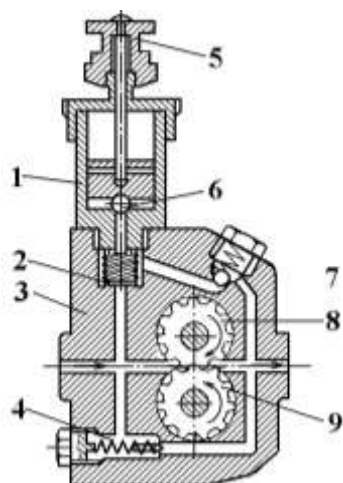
Шестеренчатый ТПН с внешним зацеплением: 1 – ручной прокачивающий насос; 2, 7 – клапаны ручной подкачки; 3 – корпус; пружина; 4 – перепускной клапан; 5 – рукоятка прокачивающего насоса; 6 – уплотнительный шарик; 8, 9 – ведомая и ведущая шестерни.
